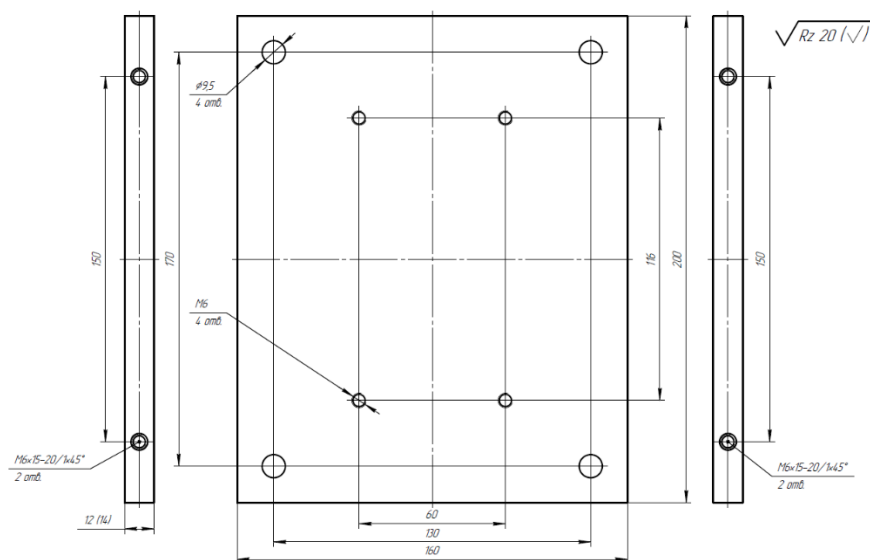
Монтажный чертеж установки пластины на горизонтальную поверхность
